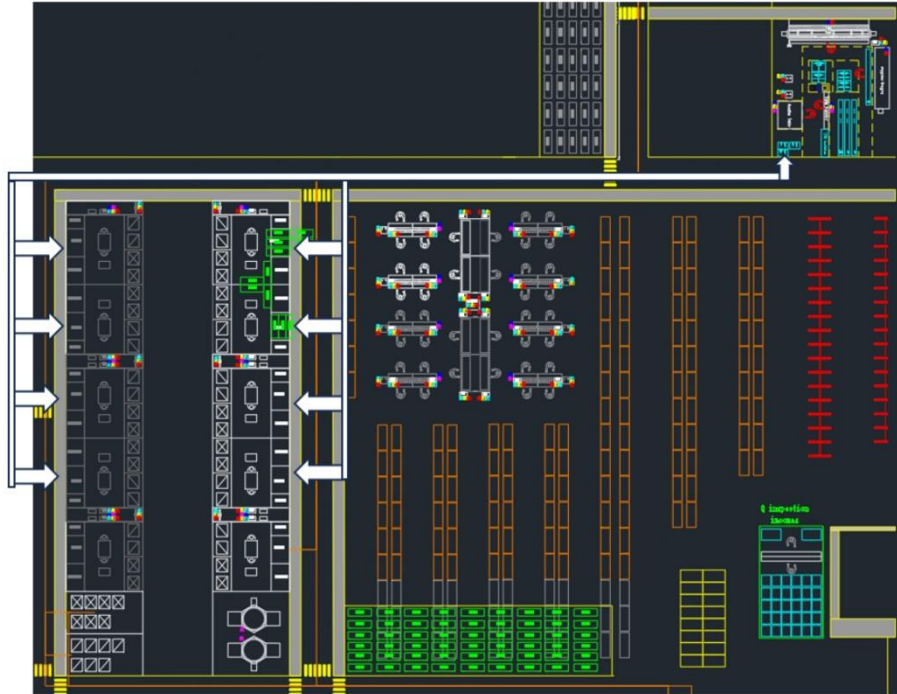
Movimentação do AGV entre os setores de Corte e Maquinagem de Perfis e Montagem de Cabines
